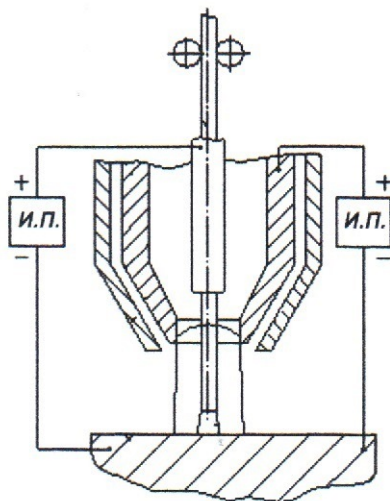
Схема сварки с использованием сопла-анода:
